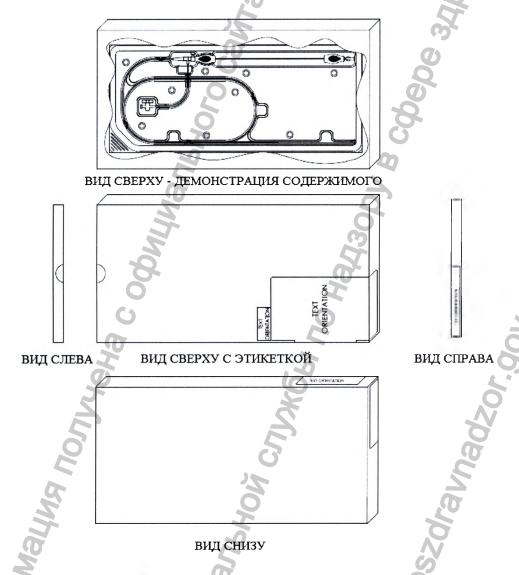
Чертеж вторичной упаковки (общий вид)
